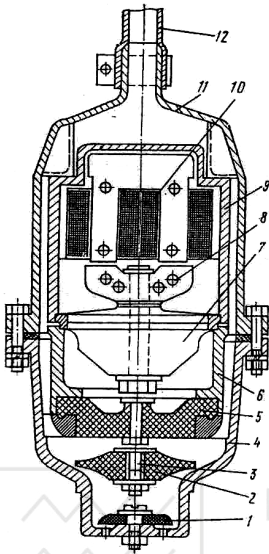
Конструкція вібраційного насоса НЕБ-1/20 з зануреним вібратором: 1- приймальний клапан; 2- робочий орган поршень; 3- шток; 4,5,6,11- деталі корпусу; 8- якор; 10- котушка електромагніта; 12- напірний шланг
